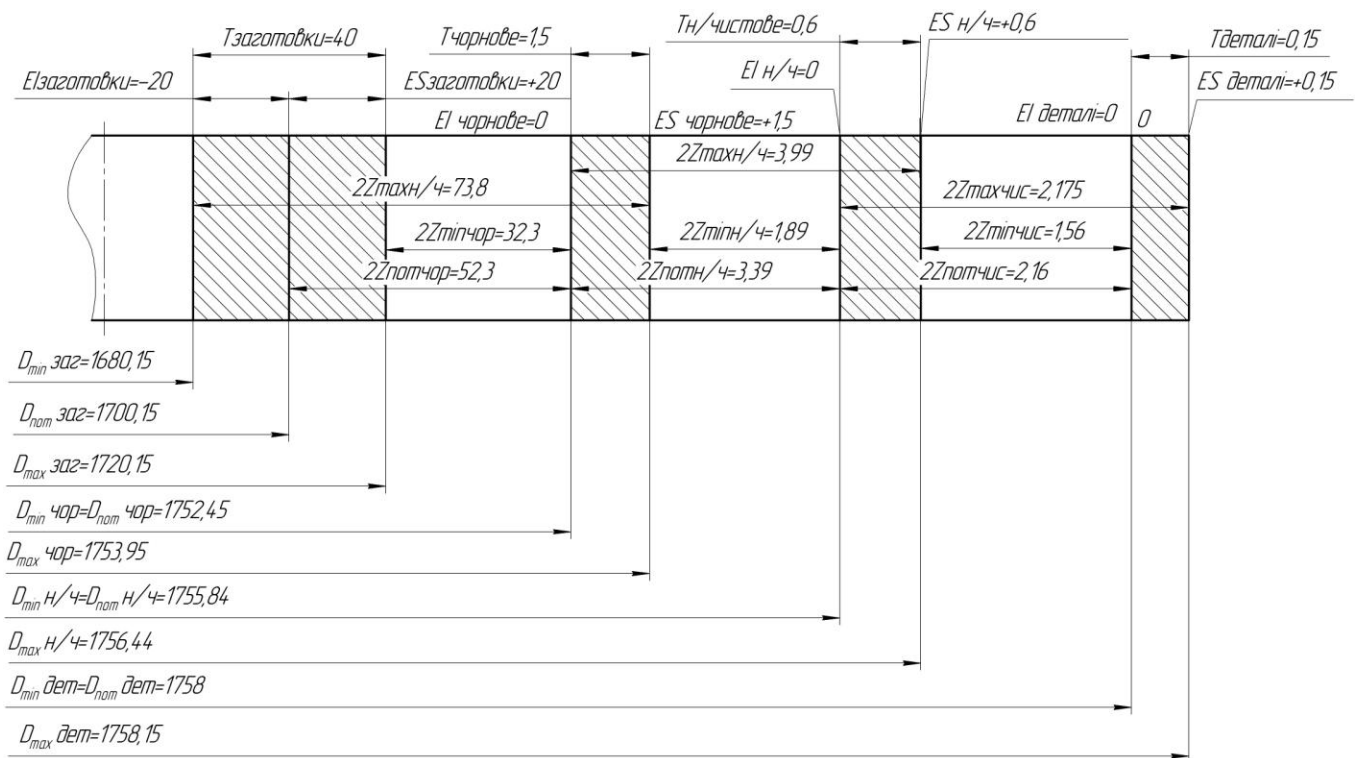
Схема розташування припусків і допусків для поверхні Ø1758H7
